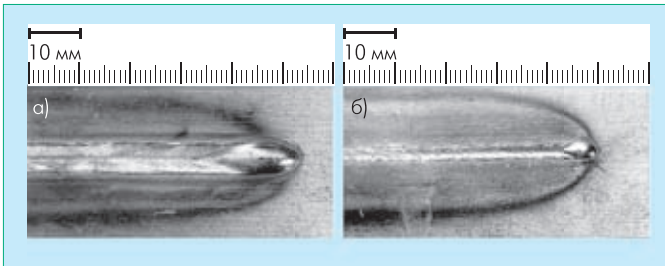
Внешний вид сварочной ванны при резке выключении лазерного пучка с лицевой стороны (а) и с обратной стороны (б) шва на стали 12ХН4МДА при проплавлении пластины толщиной 12 мм с мощностью 10,5 кВт и скоростью сварки 10 мм/с
